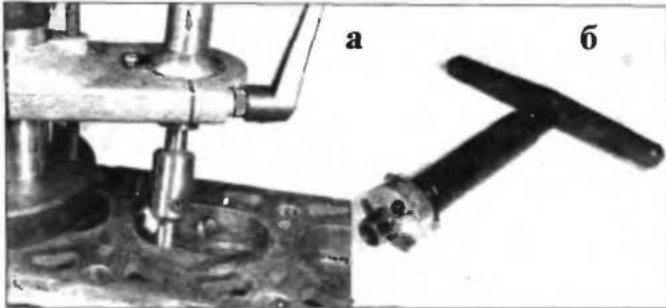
Резцовые головки для ремонта седел клапанов: а — с одним резцом; б — с несколькими резцами
